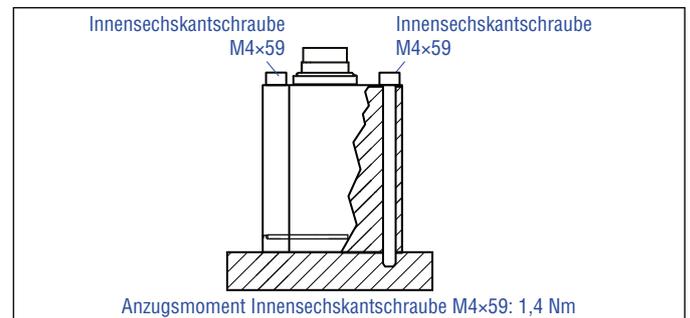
Befestigung mittels Innensechskant-Schrauben M4x59
